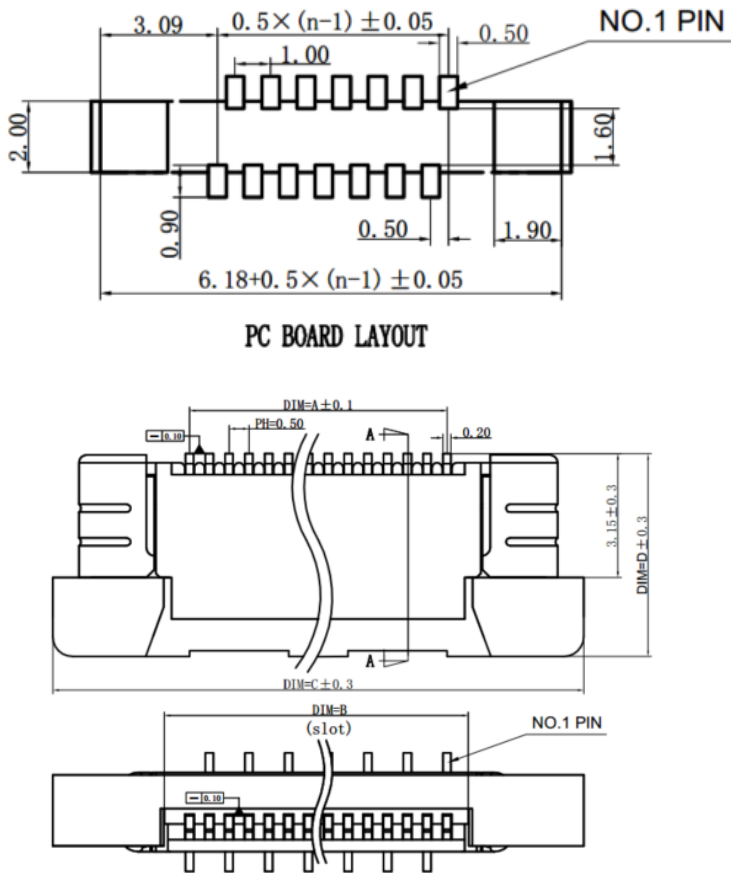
间距 0.5mm 立式双排 30PIN PCB 封装图
